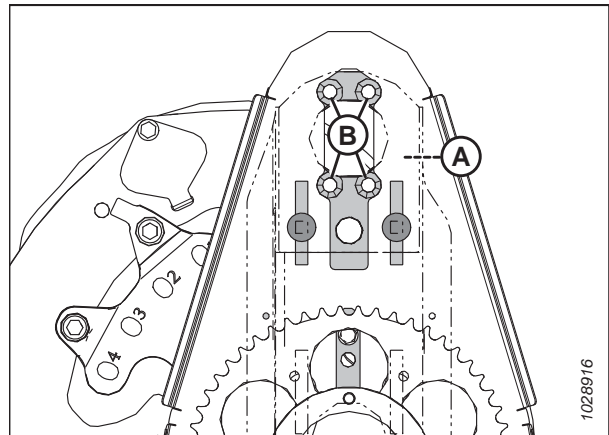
Befestigungsbohrungen des Haspelantriebsmotors
